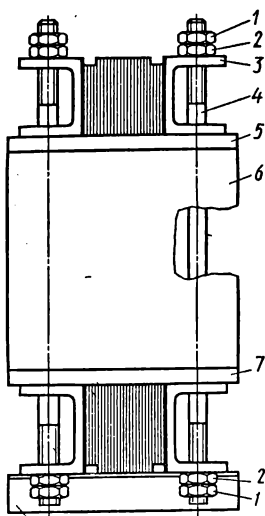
Прессовка обмоток вертикальными шпильками и ярмовыми балками трансформаторов I и II габаритов:
